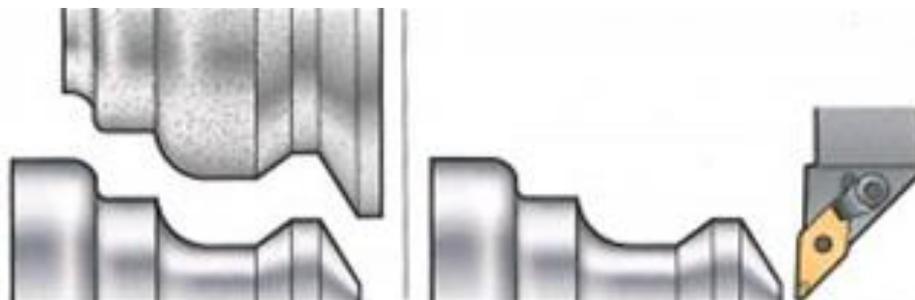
Изготовление детали методами шлифования и «твердого точения»
